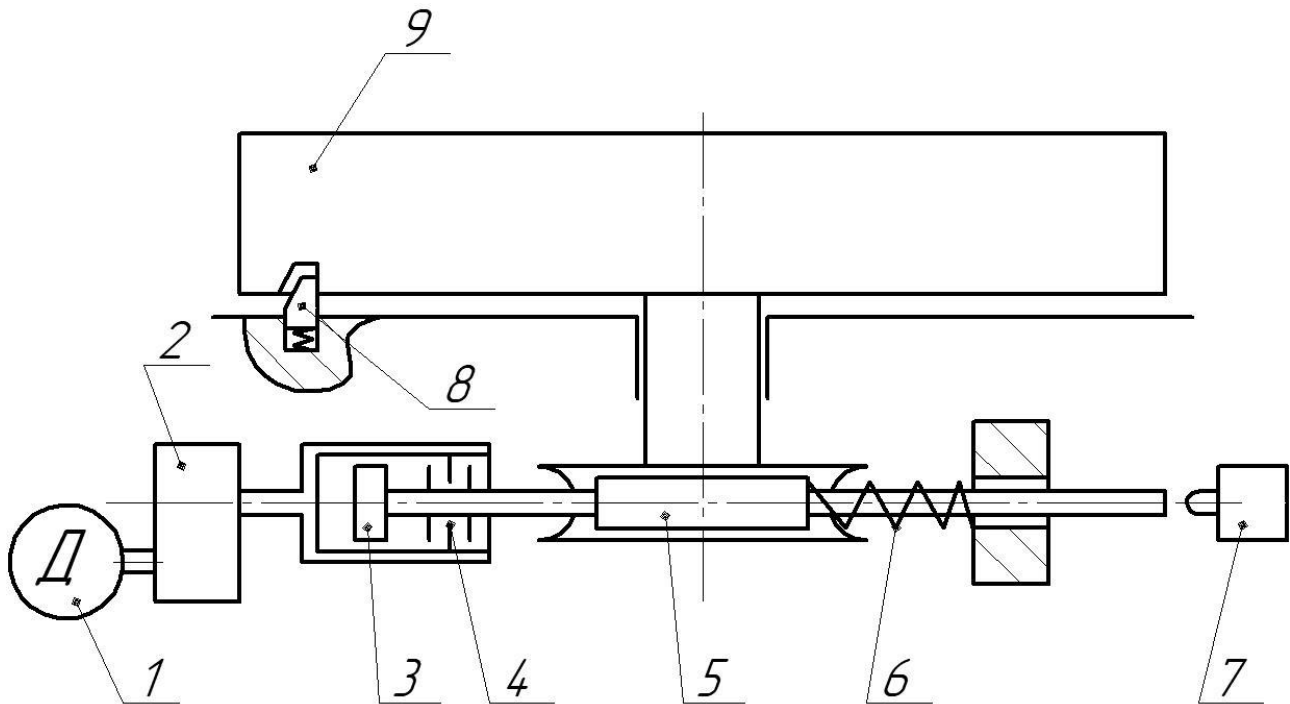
Конструктивна схема поворотного стола багатопиндельного верстата
